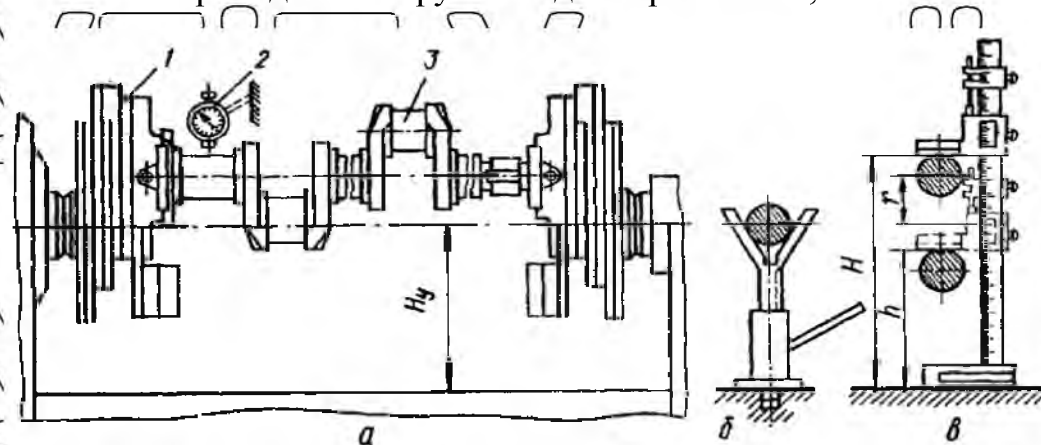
Схема установки колінчастого вала на верстаті обробки
